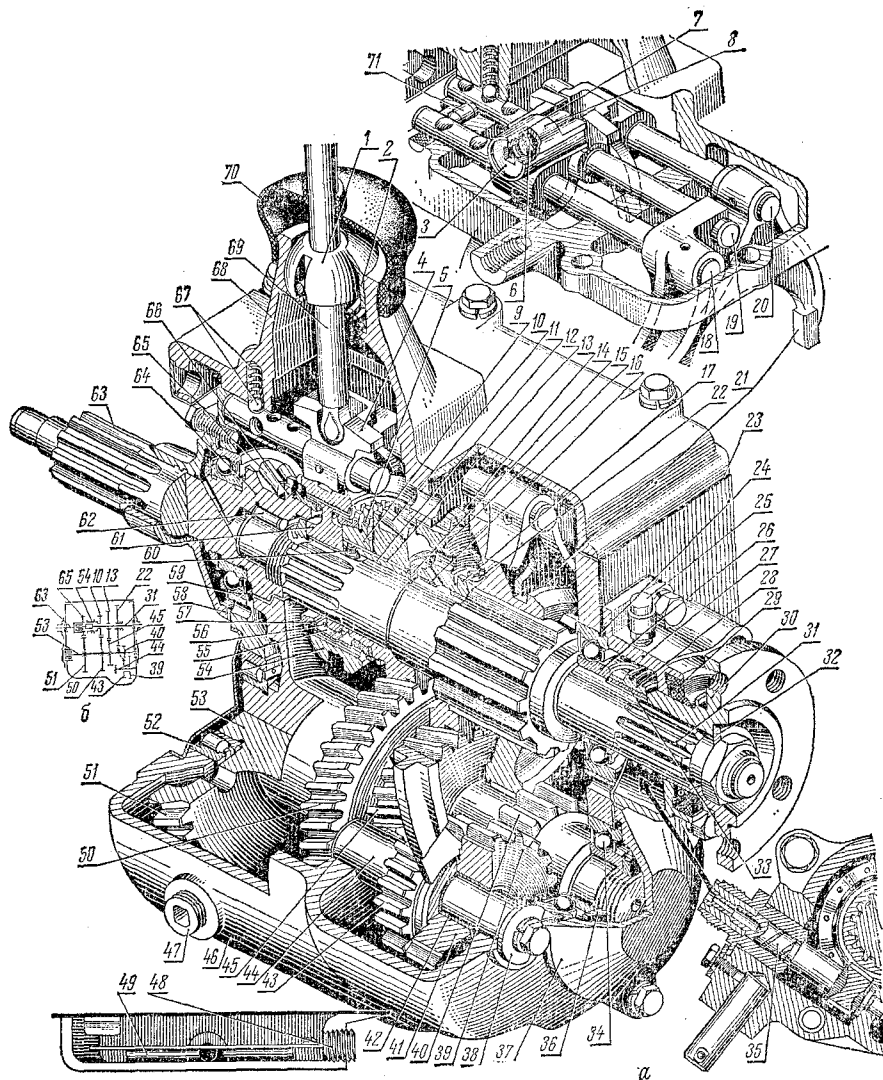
Коробка передач автомобиля ГАЗ-53А:
